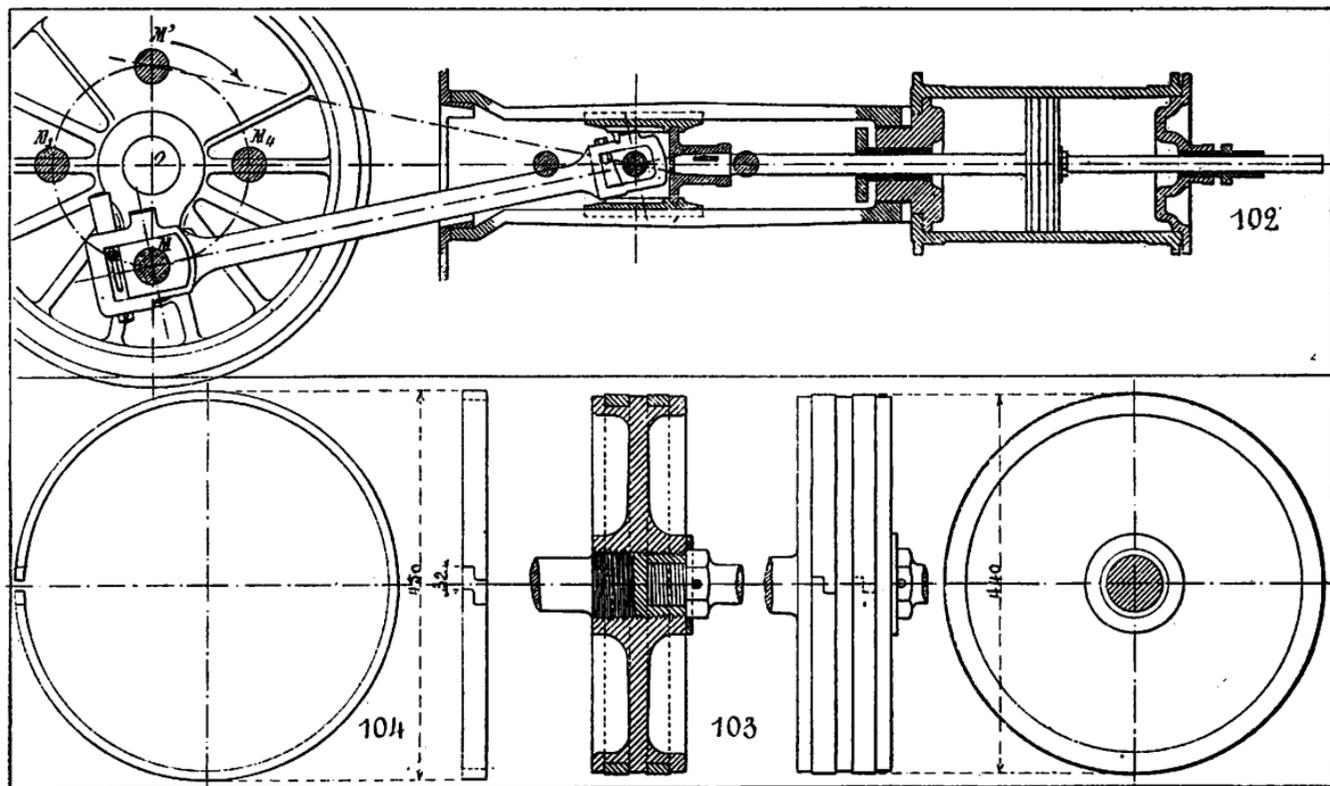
Transmission du mouvement du piston. — Fig. 103. Piston. — Fig. 104. Segment de piston.
